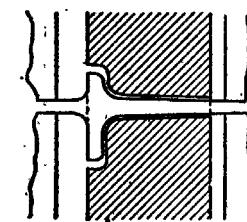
Расположение калибра на валках для прокатки тавровой стали и положение выводных проводок
